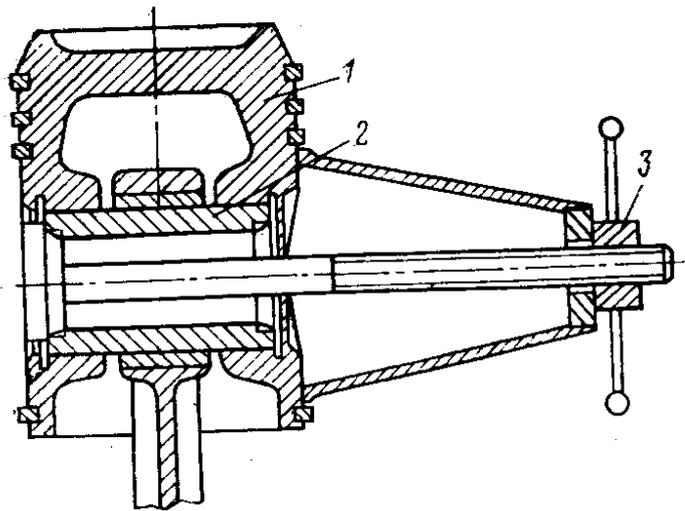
Приспособление для выпрессовки поршневого пальца
